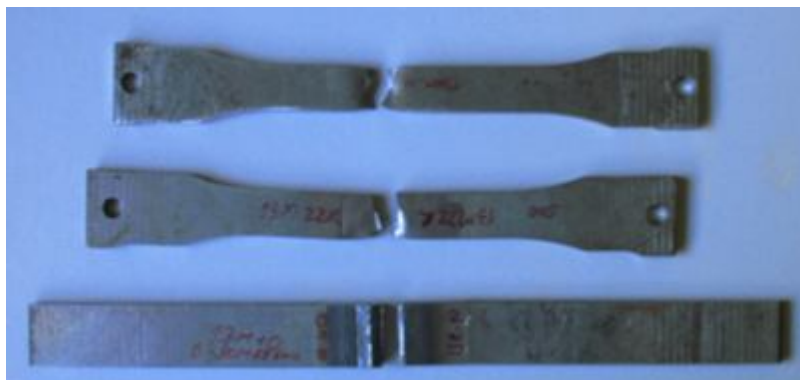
Aspecto de diferentes tipos de provetes fracturados.
